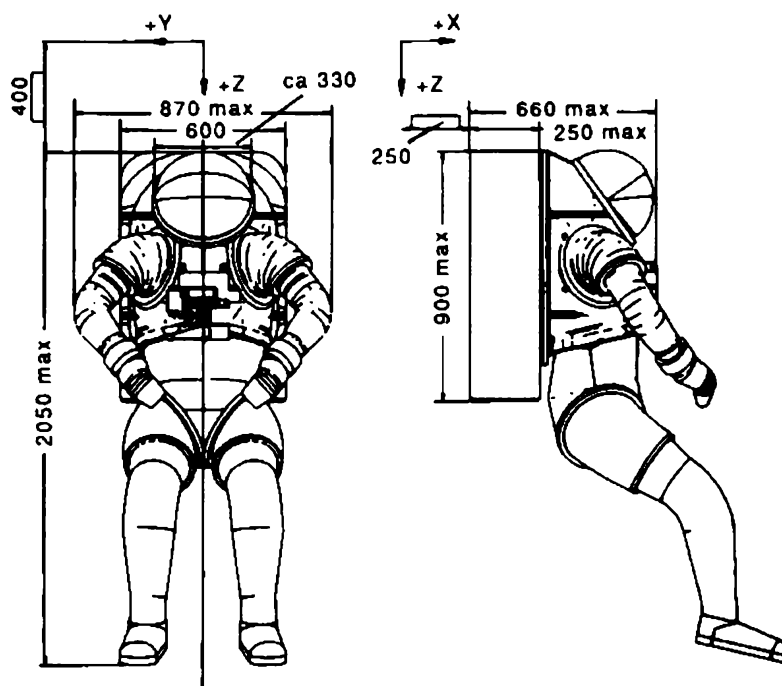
Габаритные размеры скафандра ESSS
